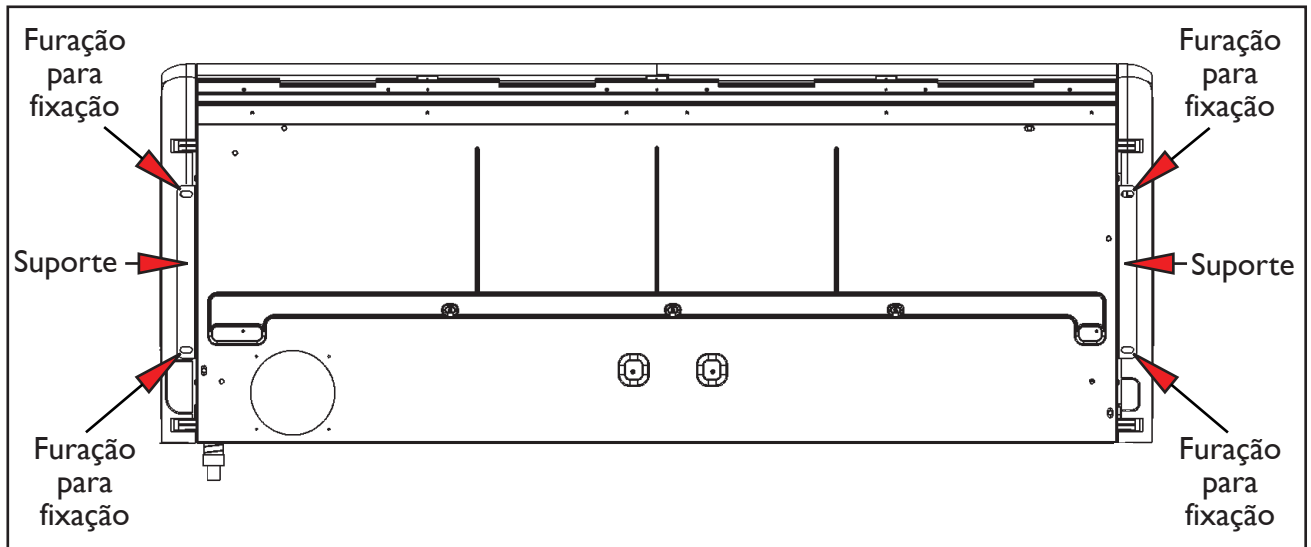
SUPORTES E FURAÇÃO PARA FIXAÇÃO
